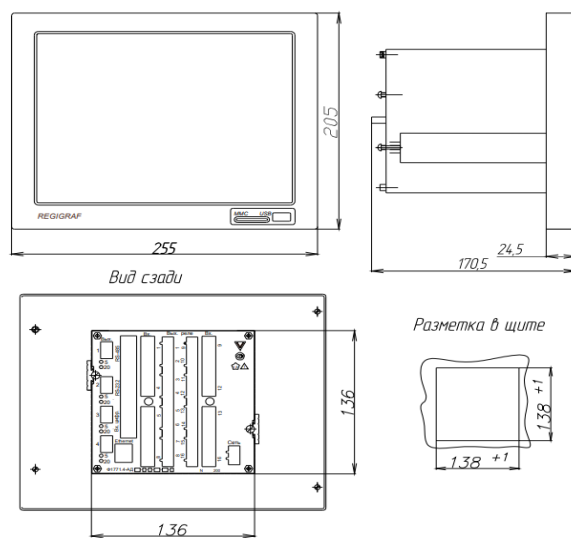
Габаритный чертёж прибора и вырез в щите
